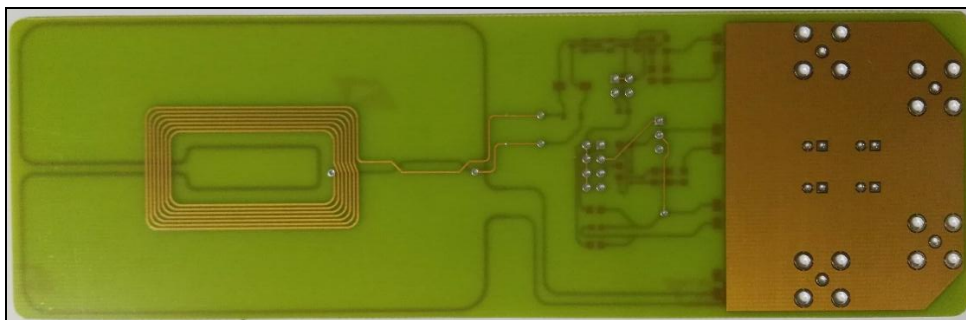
PCB PICC de Referencia N° 5 – Capa BOTTOM
